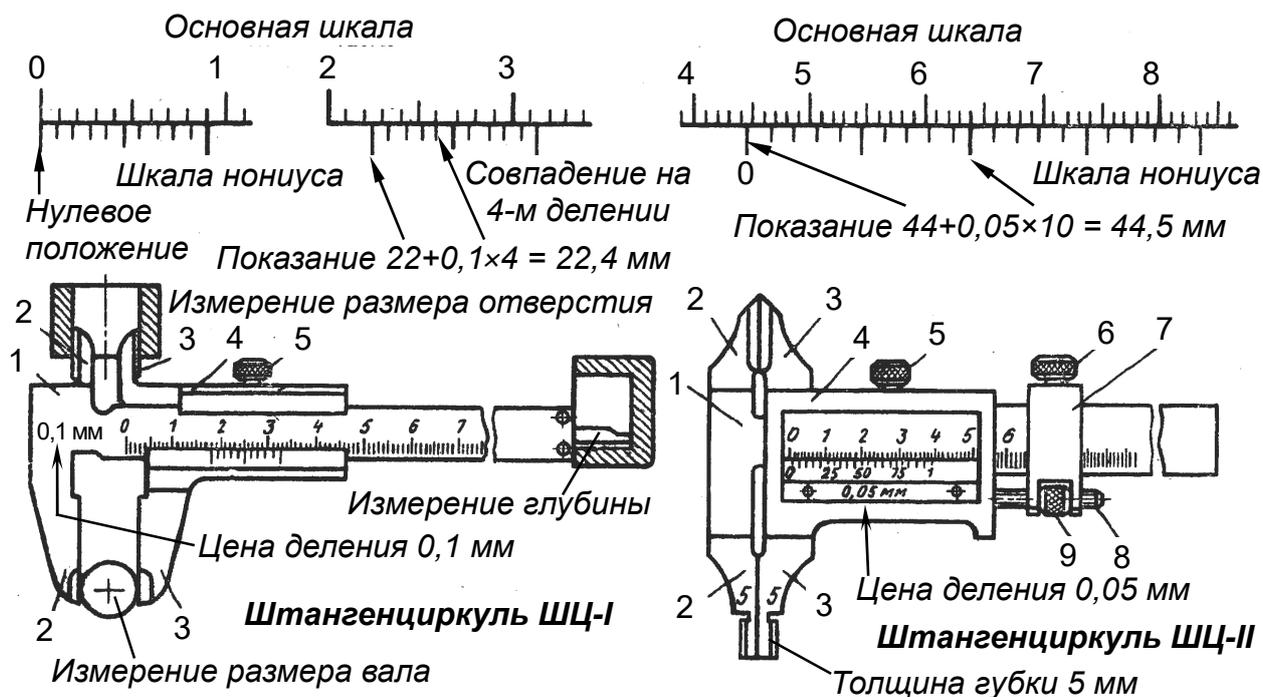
Конструкции штангенциркулей и выполнение измерений:
